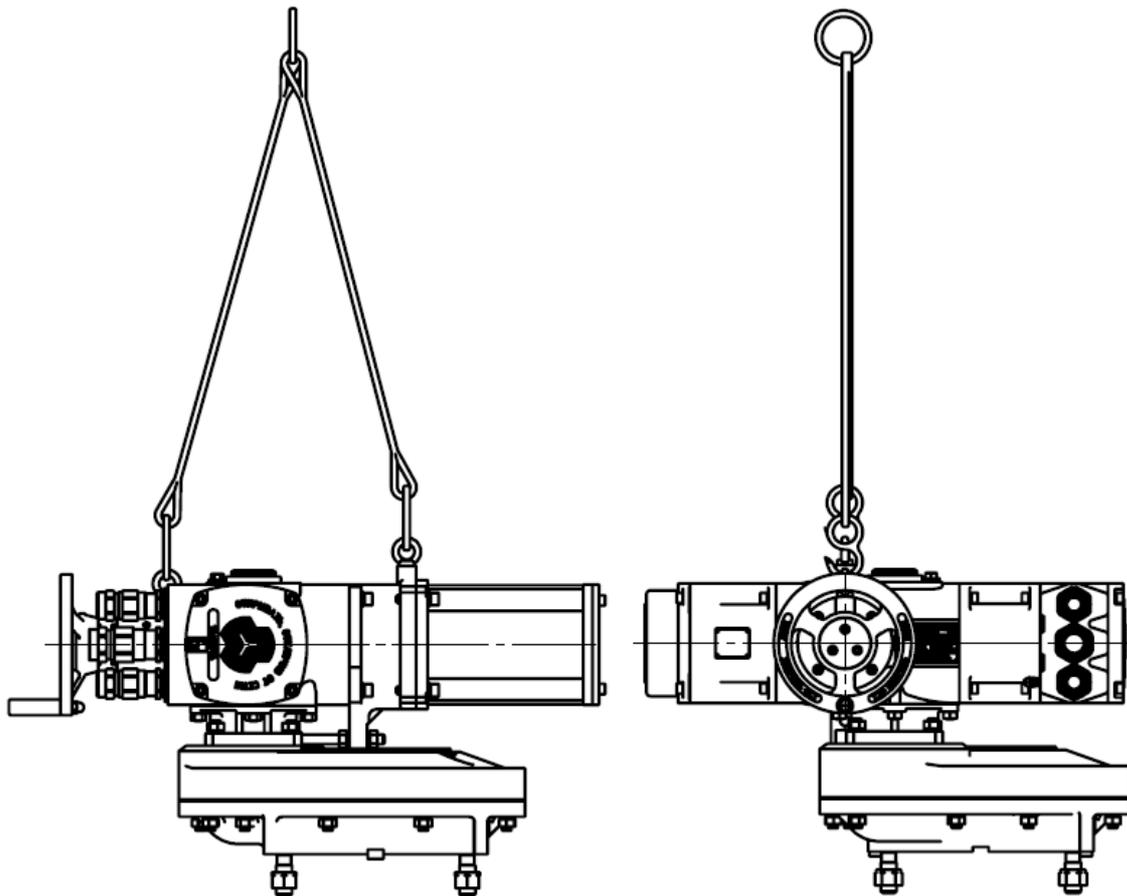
в – Схема строповки привода конструктивной схемы 410
